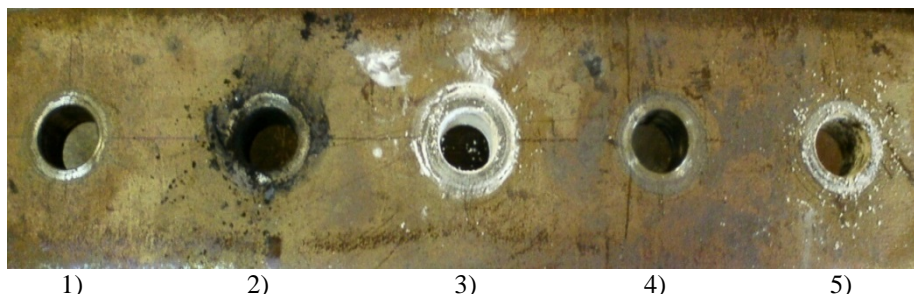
Внешний вид болтов с нанесенными смазками в собранном соединении с вариантами смазок:
